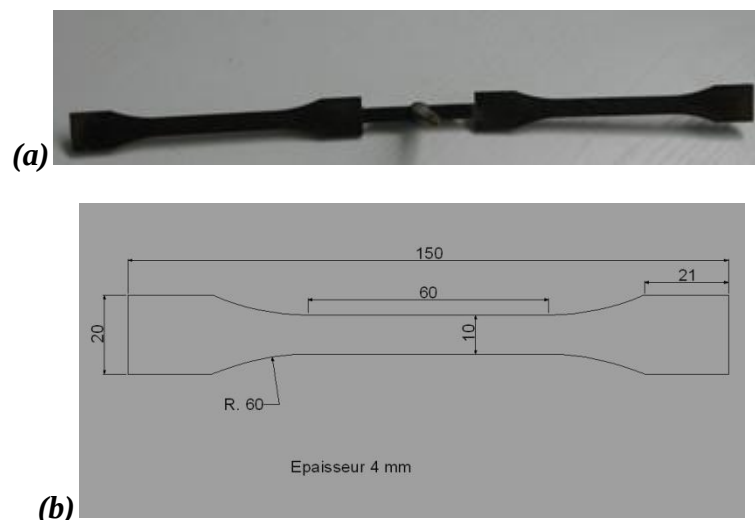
(a) Schéma de 2 éprouvettes après injection, (b) Dimensions de l'éprouvette
